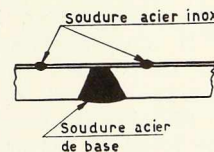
Soudure de bande en acier inoxydable.
